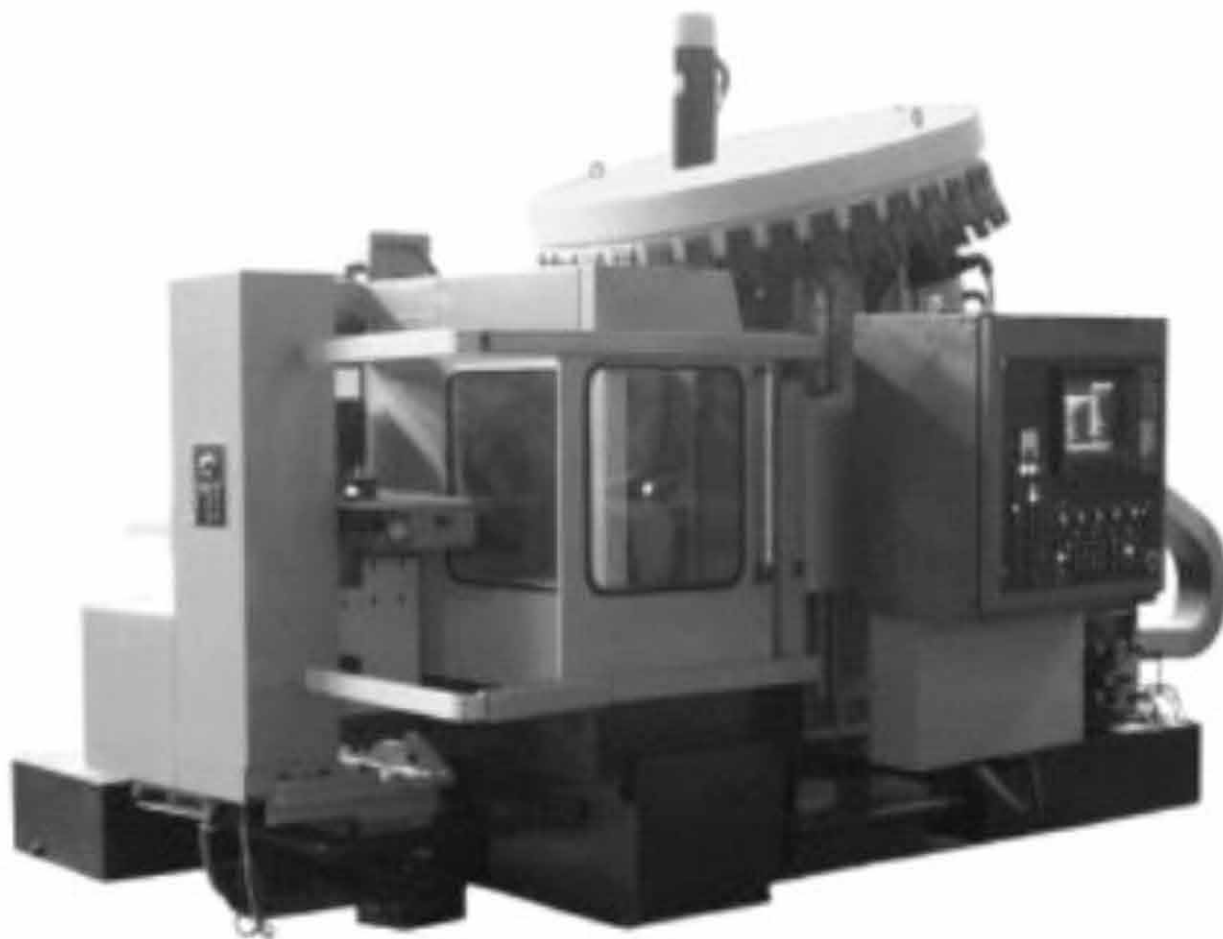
Загальний вигляд верстата 320ПМФ4
